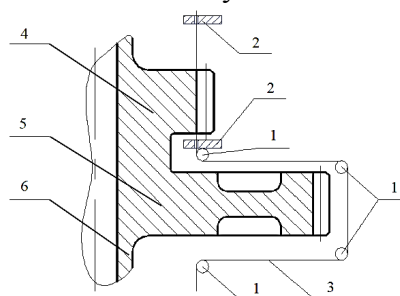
Схема электроэрозионной обработки цилиндрического эвольвентного закрытого венца цельного блока зубчатого колеса: 1 – ролики; 2 – алмазная направляющая; 3 – проволока; 4 – закрытый венец; 5 – открытый венец; 6 – цельный блок зубчатых колес
